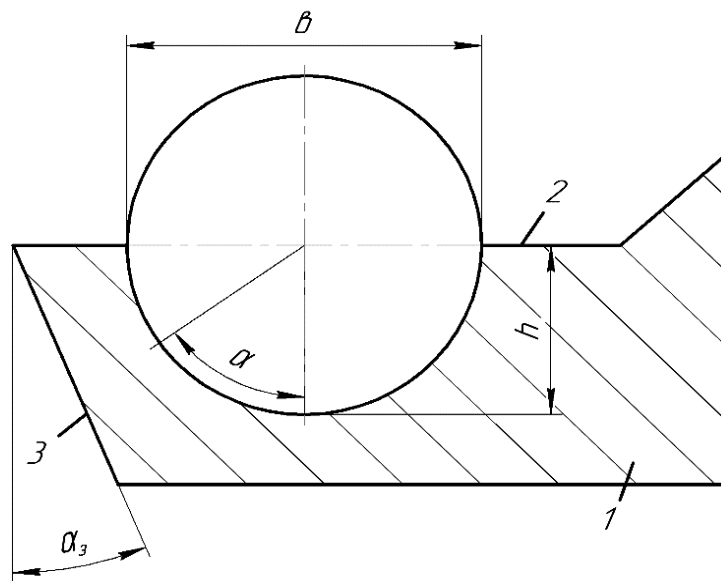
Профиль канавки на передней поверхности резца: 1 – резец; 2 – передняя поверхность; 3 – задняя поверхность; b – ширина канавки; h – глубина канавки; α – угол заточки задней поверхности резца
